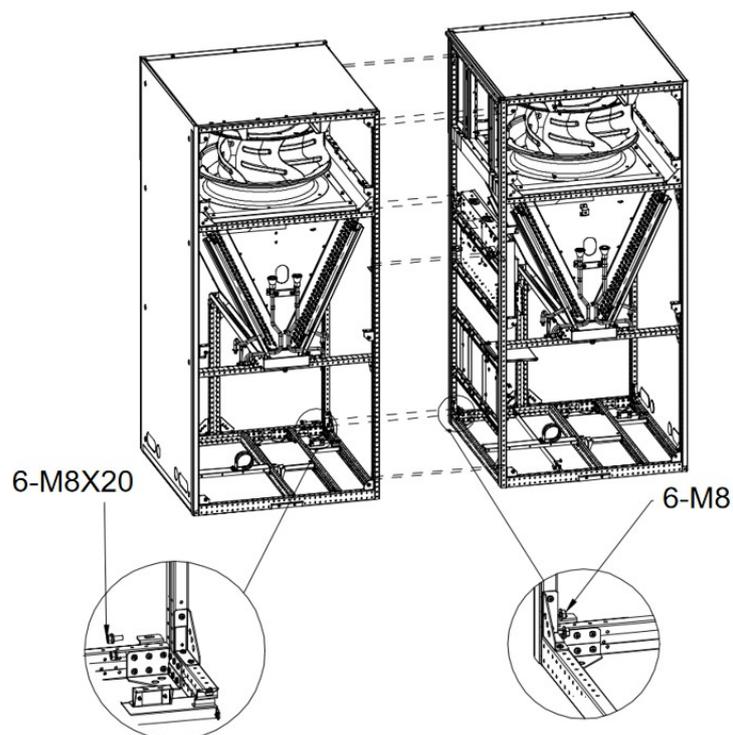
Положение винтов для разборки внутреннего блока с двумя модулями
